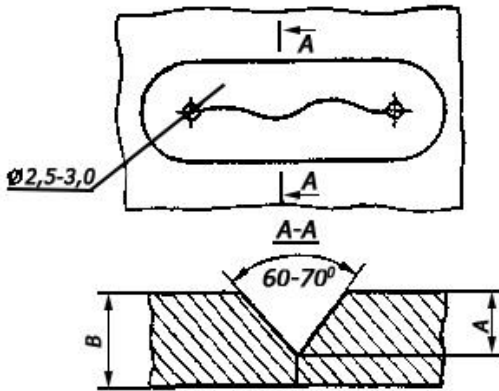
Обробка тріщини під зарівнювання епоксидною композицією
